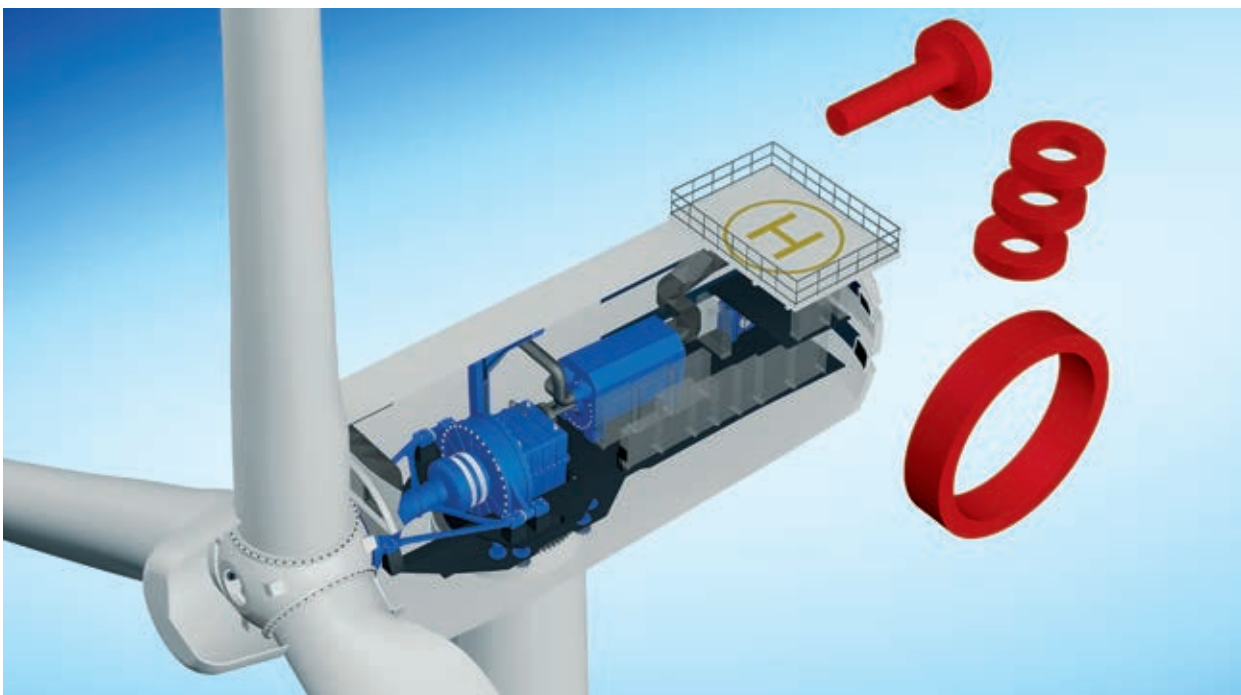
Blick in das Maschinenhaus einer modernen Windenergieanlage
